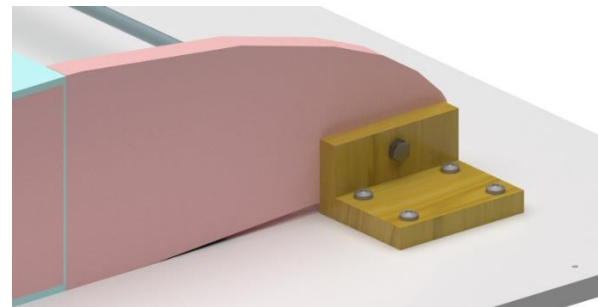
Odklopené křídlo zaistené pomocou skrutky
